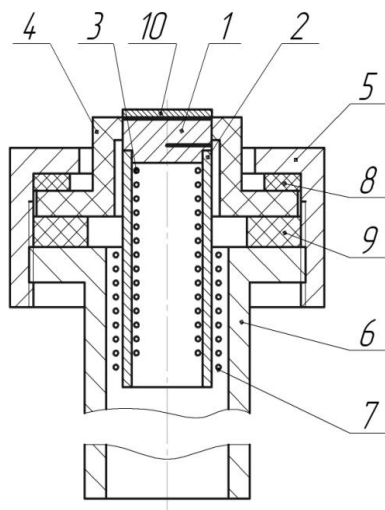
Конструкция рабочего элемента: 1 – тепловыделяющая втулка; 2 – корпус нагревателя; 3 – электронагреватель РЭ; 4 – стекловолоконитовая шайба; 5 – прижимная гайка; 6 – корпус РЭ; 7 – охранный нагреватель; 8, 9 – уплотнения; 10 – пористое покрытие
